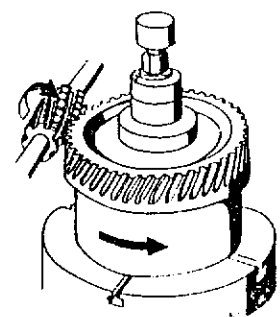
Fresado de una rueda frontal con dientes inclinados por el procedimiento de rodamiento.
